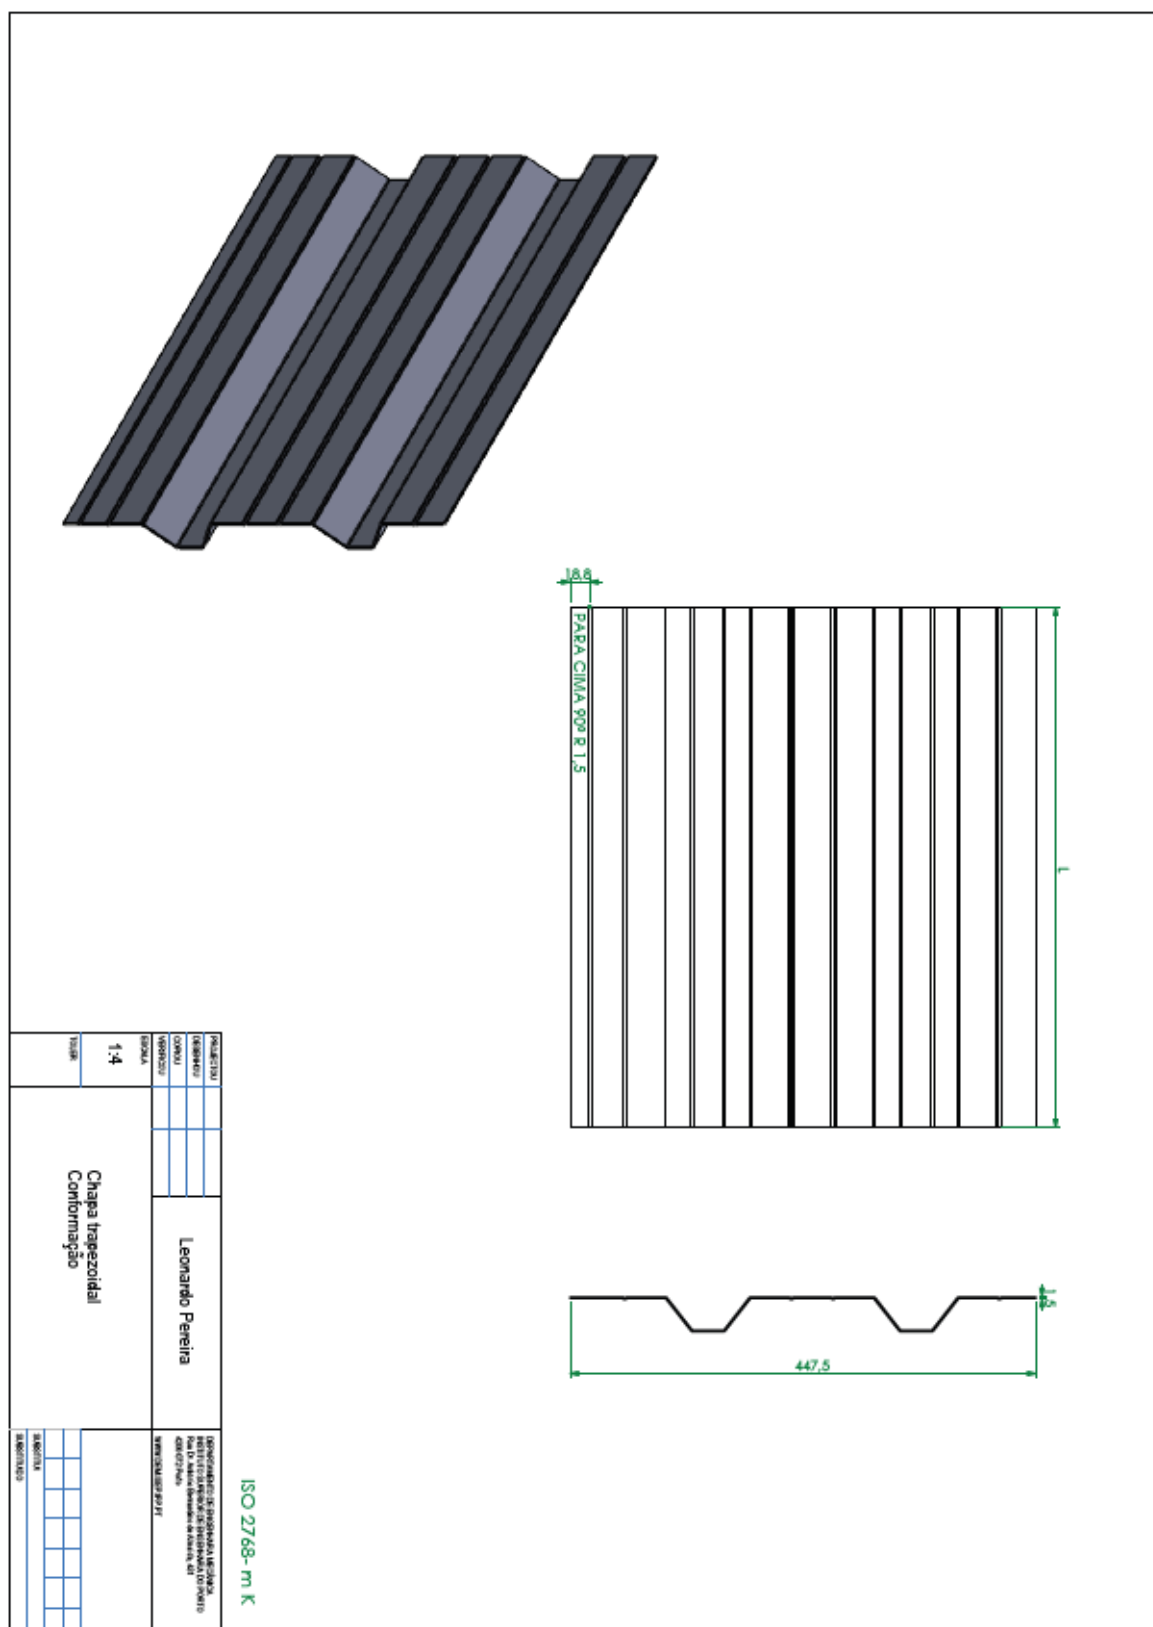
Desenho técnico para processo da chapa trapezoidal
